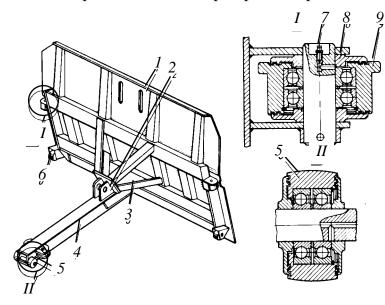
Задняя стенка ковша: I — щит; 2 — проушина; 3 — раскос; 4 — толкатель; 5, 6, 9 — ролики; 7 — масленка; 8 — шайба; I, II — разрез направляющих роликов
